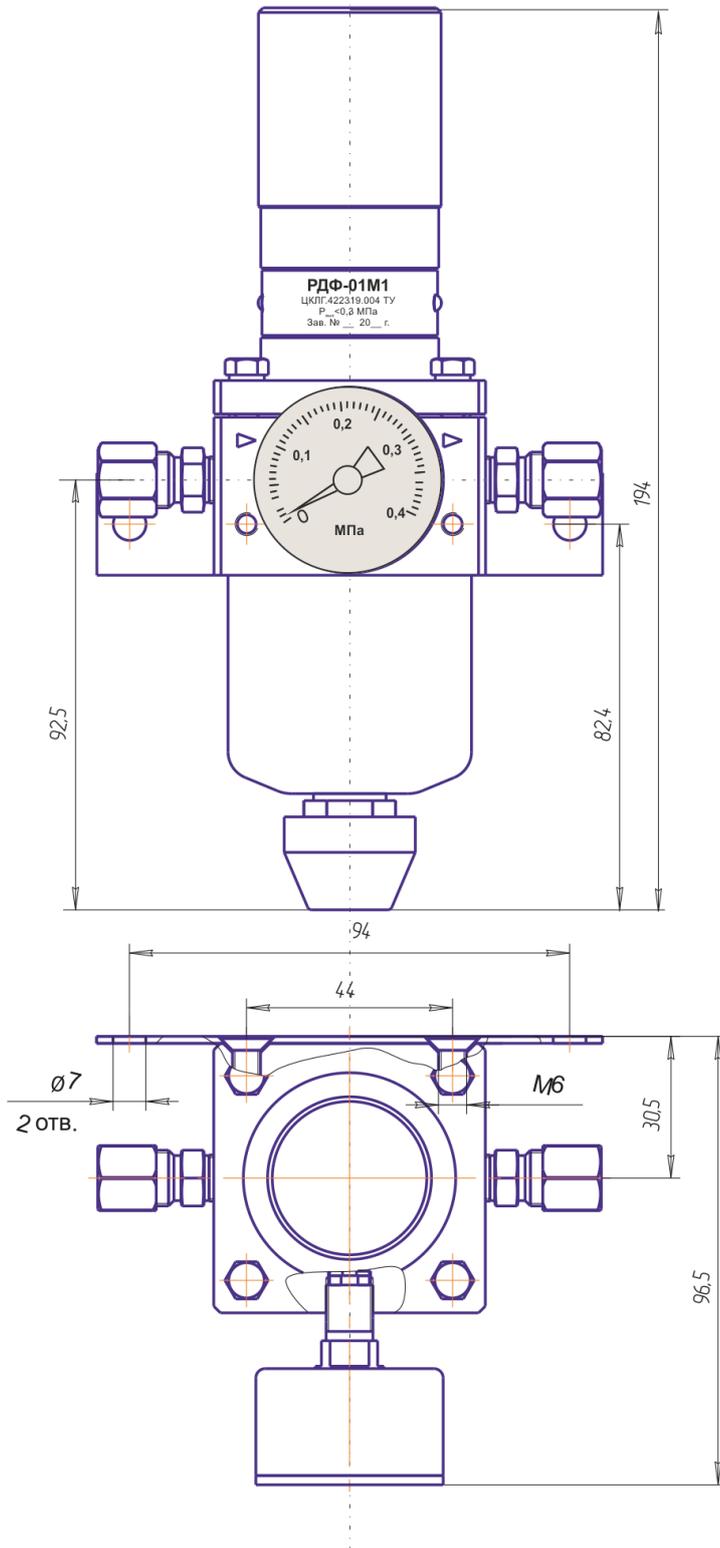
Габаритные и присоединительные размеры редуктора
